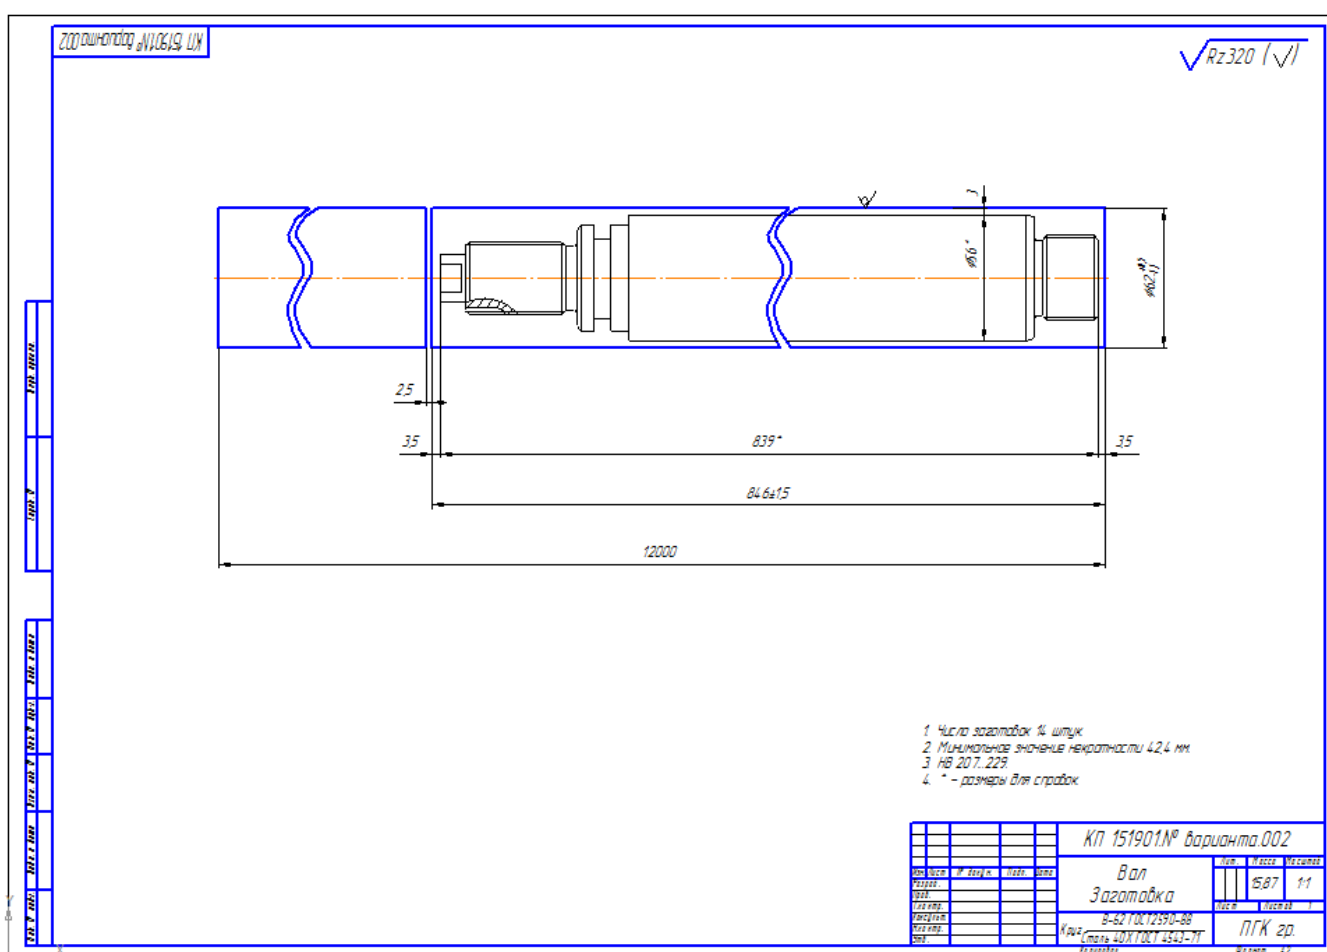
Чертеж заготовки детали «Шток».
